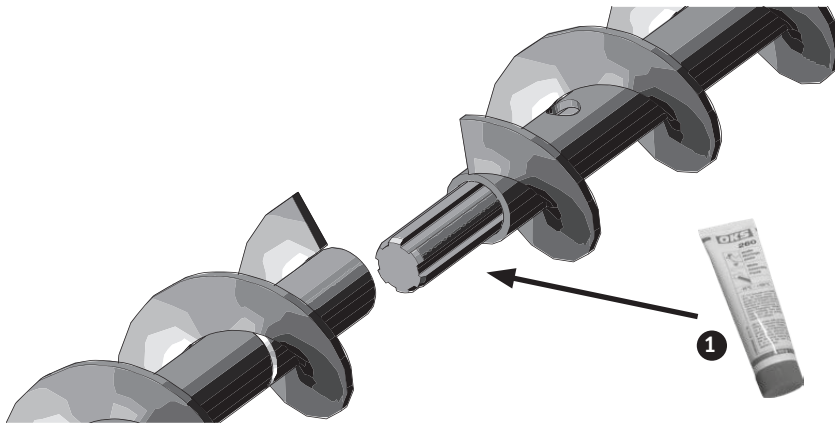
Verbindungsstücke großzügig mit Gleitfett einstreichen und Schnecke passgenau ganz zusammenführen
